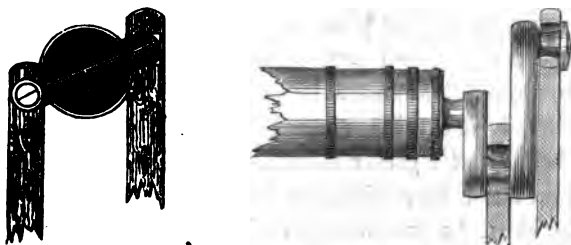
Transmission de mouvement de l'arbre de la roue à l'arbre des tambours.
